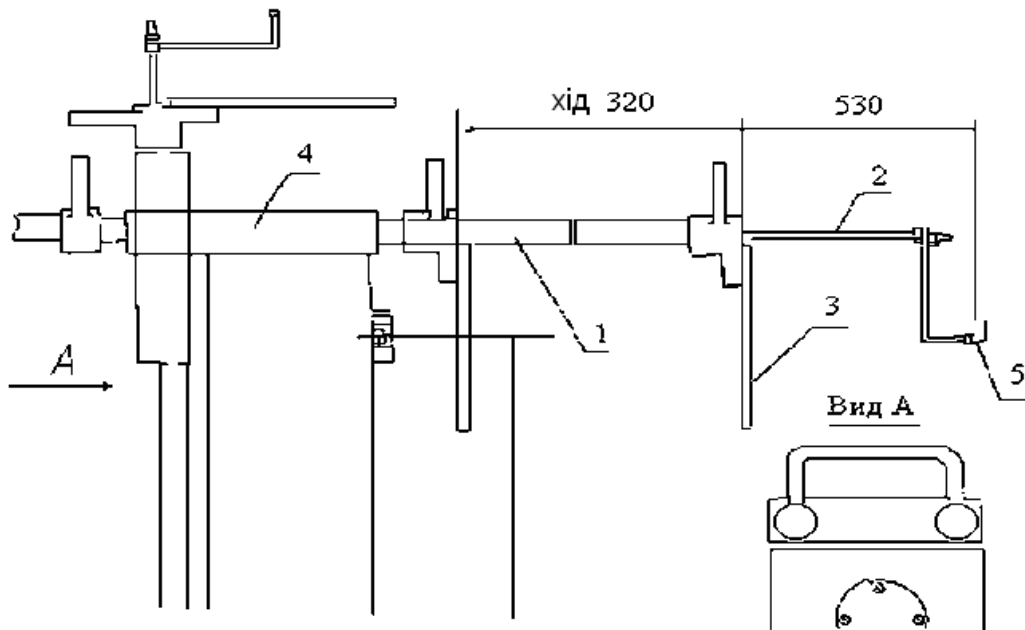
Стійка з ползками: 1 – ползки; 2 – лінійка-щуп; 3 – шкала; 4 – стійка; 5 – упор
